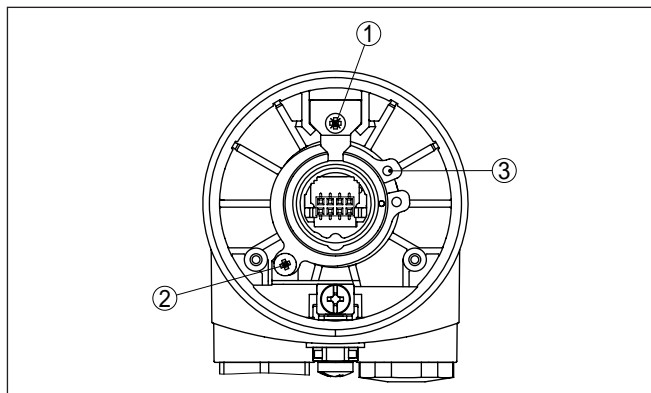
Положение винтов и стопорного кольца, например, на пластиковом корпусе
